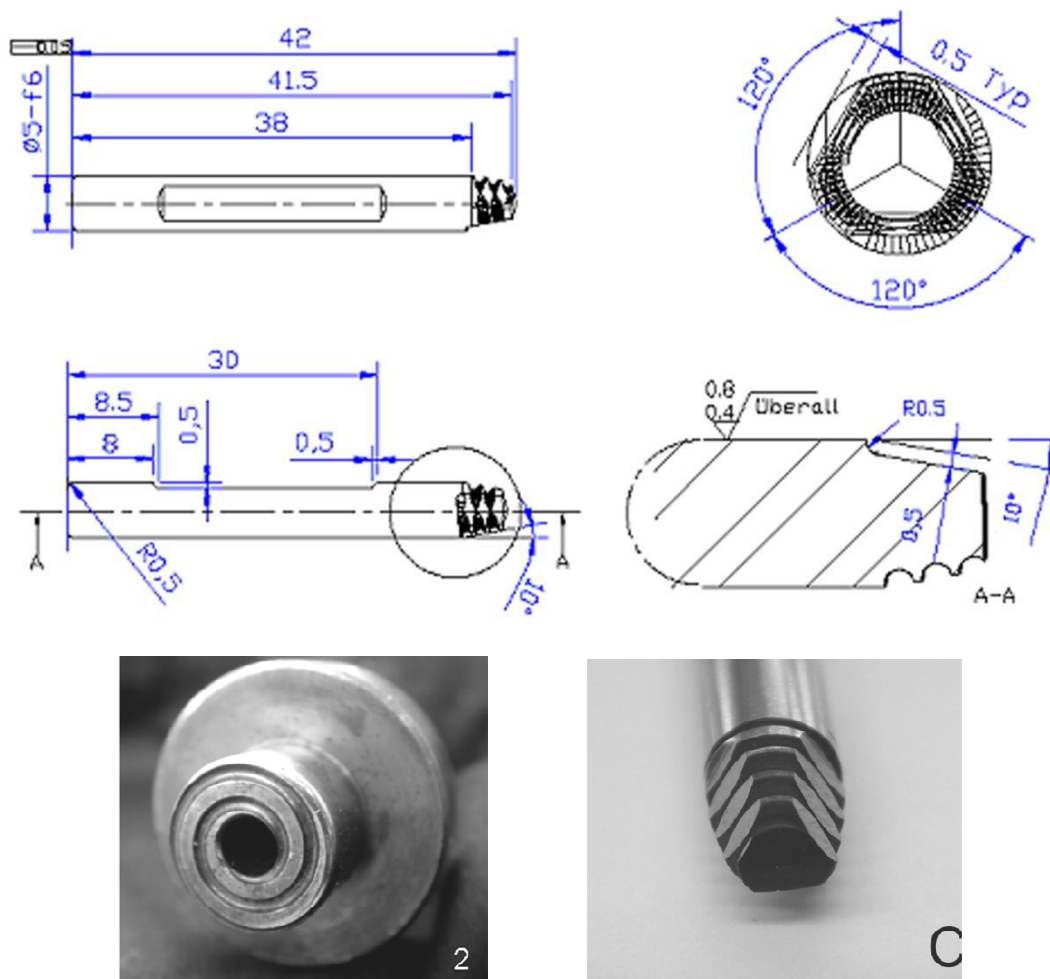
Perfil geométrico e design da ferramenta *shoulder* e pino (fonte: GKSS)
